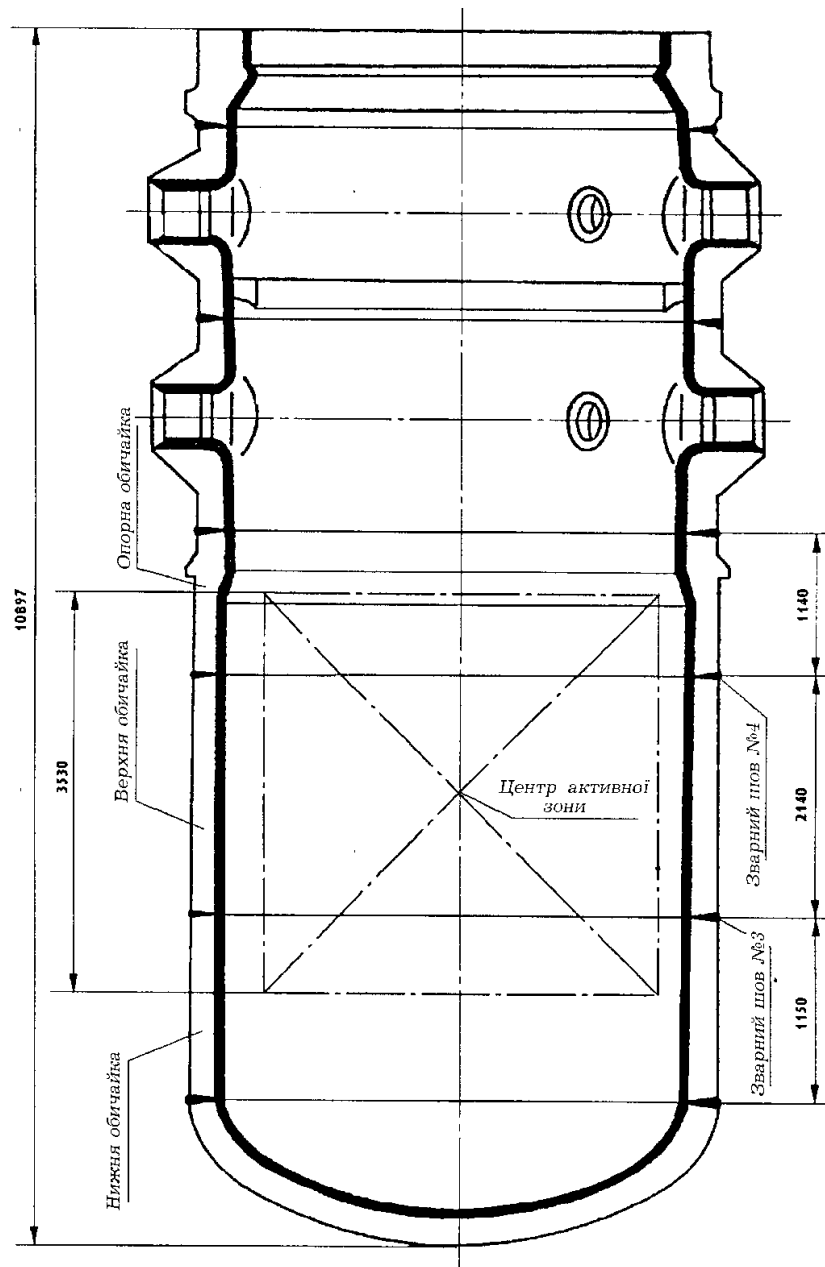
Корпус енергетичного реактора ВВЕР-1000
